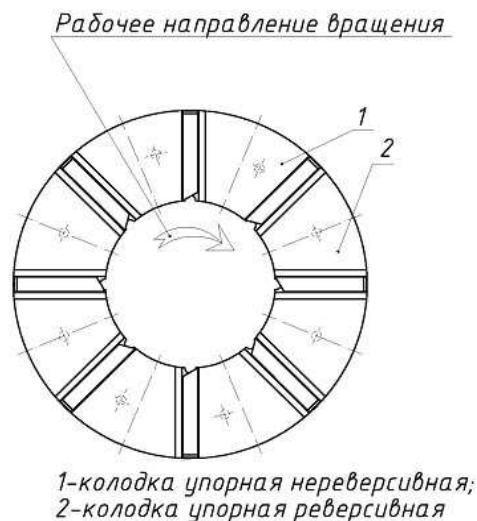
Комбинированная нерабочая упорная часть подшипника ПДУ-120/260
